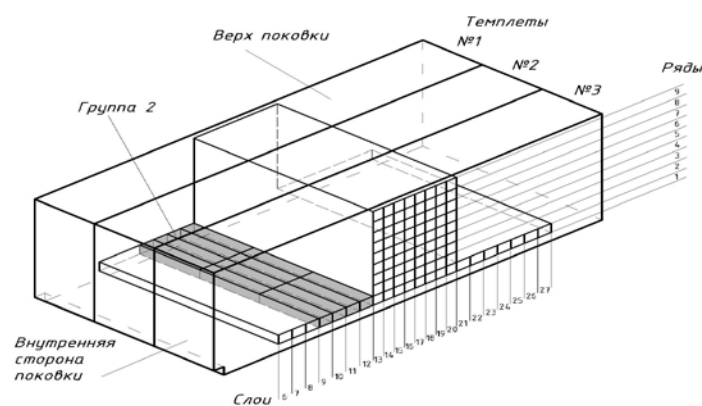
Схема вырезки образцов из темплетов 1-3 и компоновка образцов Шарпи в группы
